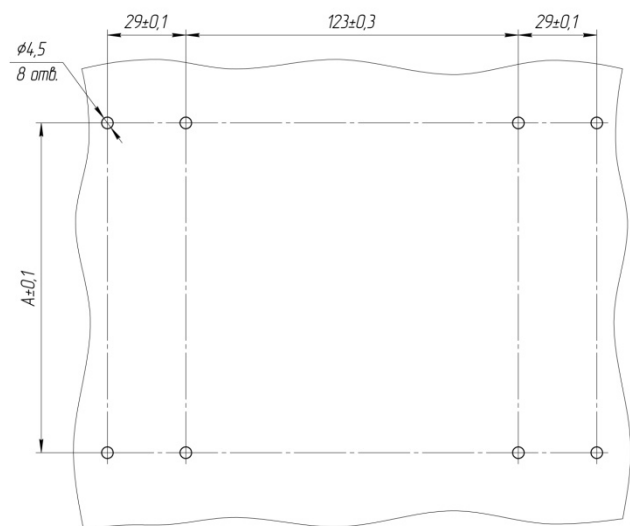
Габаритные и присоединительные размеры устройства РС83-АВ2 при внешнем монтаже, обеспечивающем его поворот вверх/вниз
